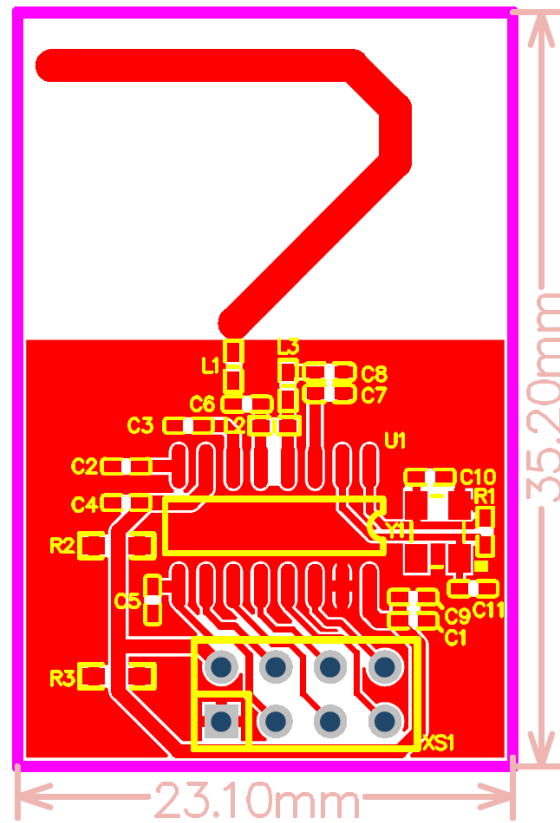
HW2000 EVB PCB (SOP16 Single Layer PCB)
